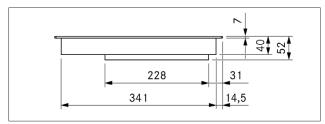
Dimensões do aparelho PKFI3, vista dianteira
